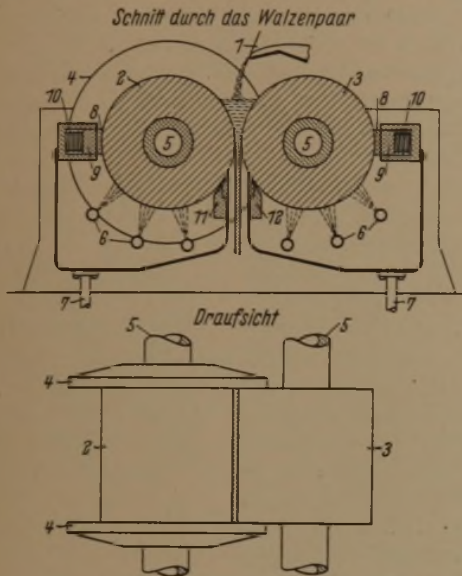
Walzenpaar mit Abschlußflanschen (Bessemer 1857).
